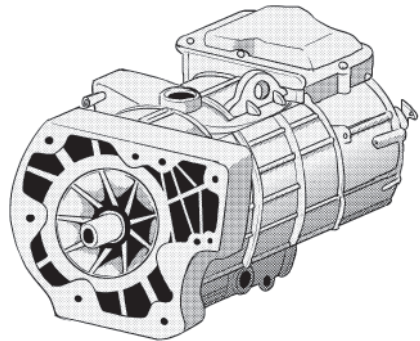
Синхронный двигатель с постоянными магнитами
